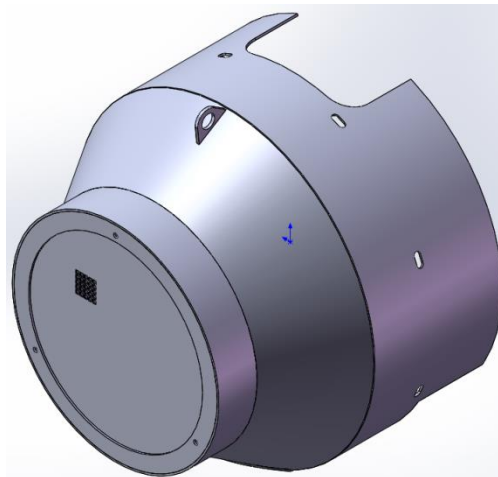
Exemplo TD Padrão Motor W22Xd (WPT) 315
